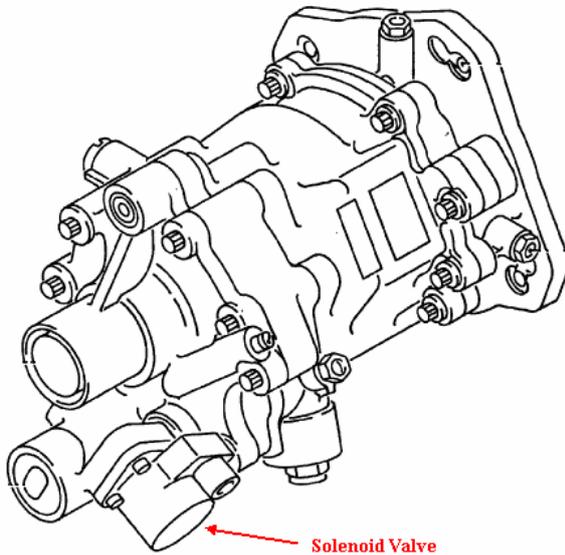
Triebwerksbetriebene Hydraulikpumpe
